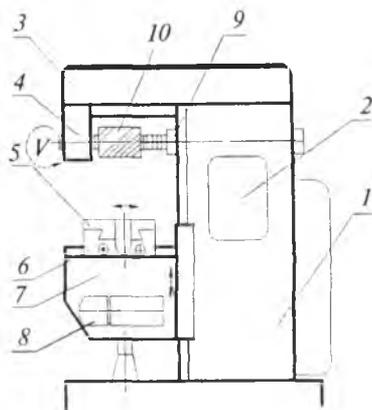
Общий вид горизонтально-фрезерного станка модели 6H82
